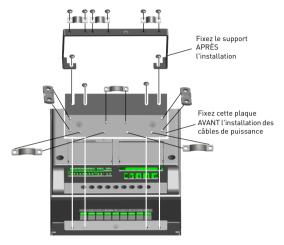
Montage de la plaque PE et du support de câble API, MI4 - MI5
